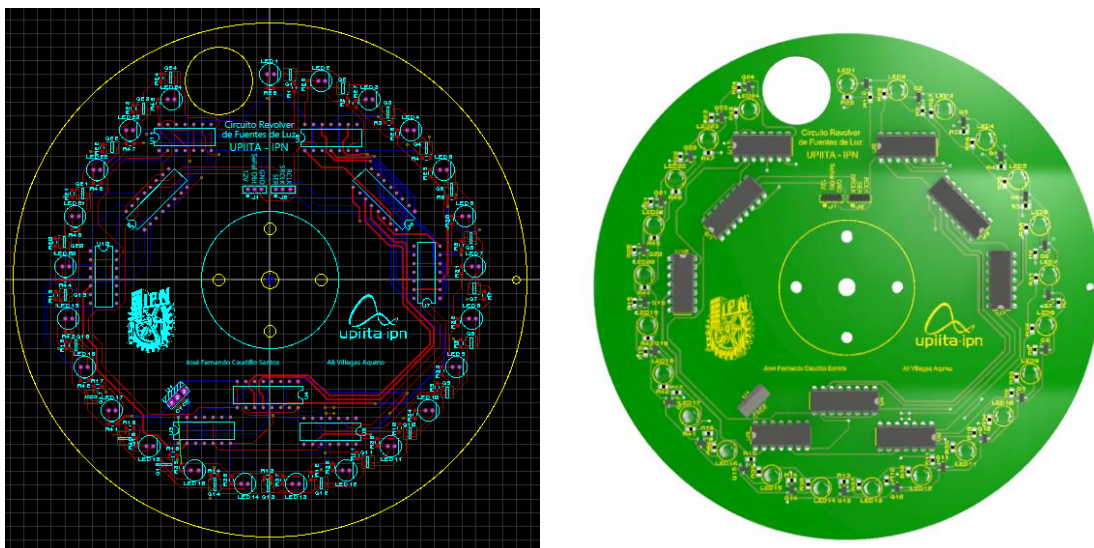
Diseño del PCB y Modelo del Revolver de Fuentes de Luz.
